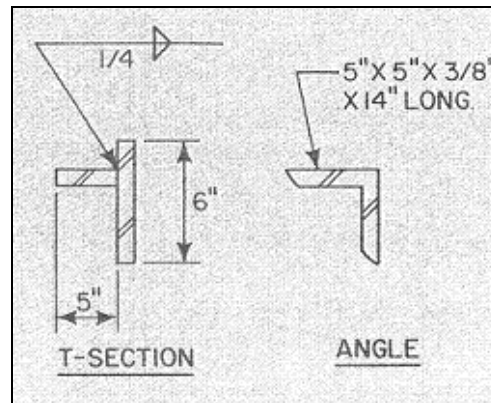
Conexión de perfiles ángulo soldados.
